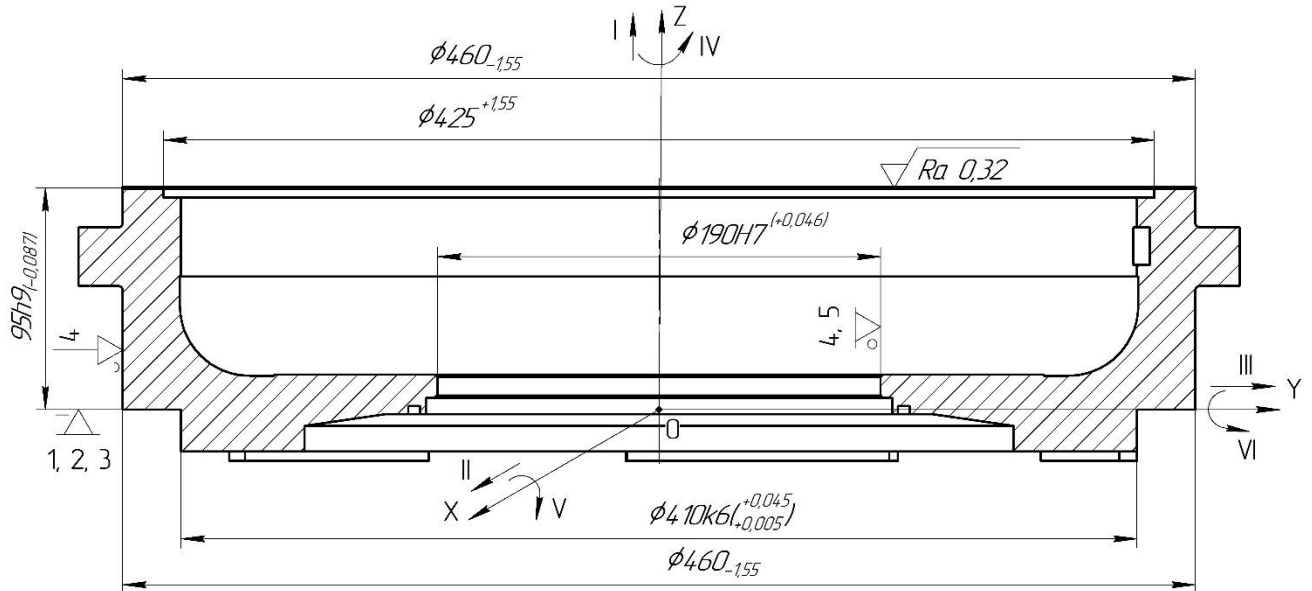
Схема установки заготовки на операції 040. Установ А
